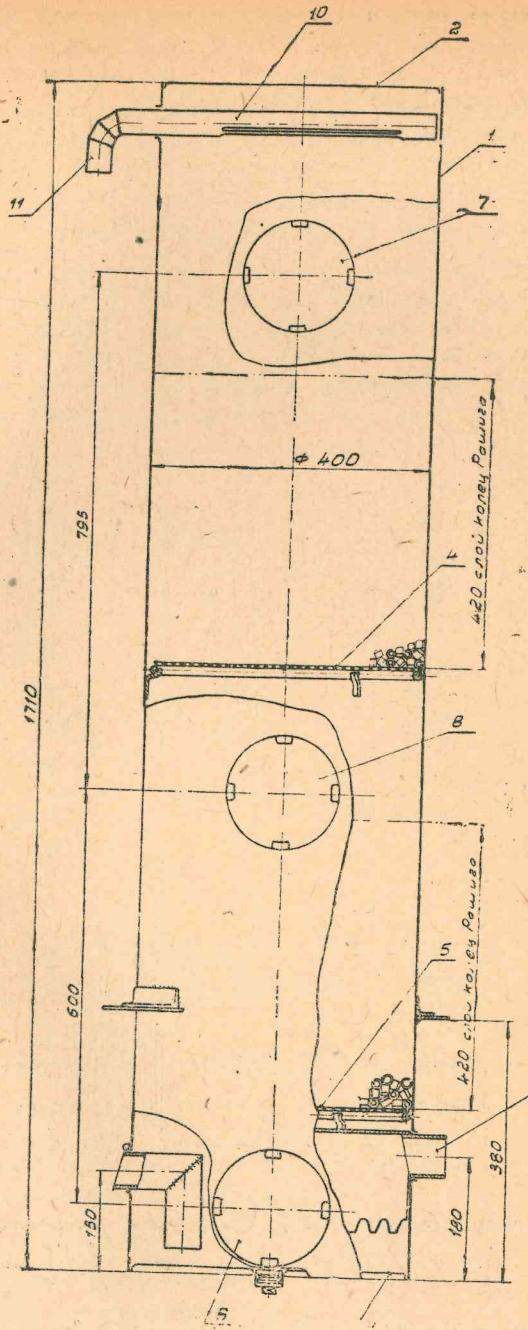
Тонкий очиститель газогенераторной установки Г-69:
